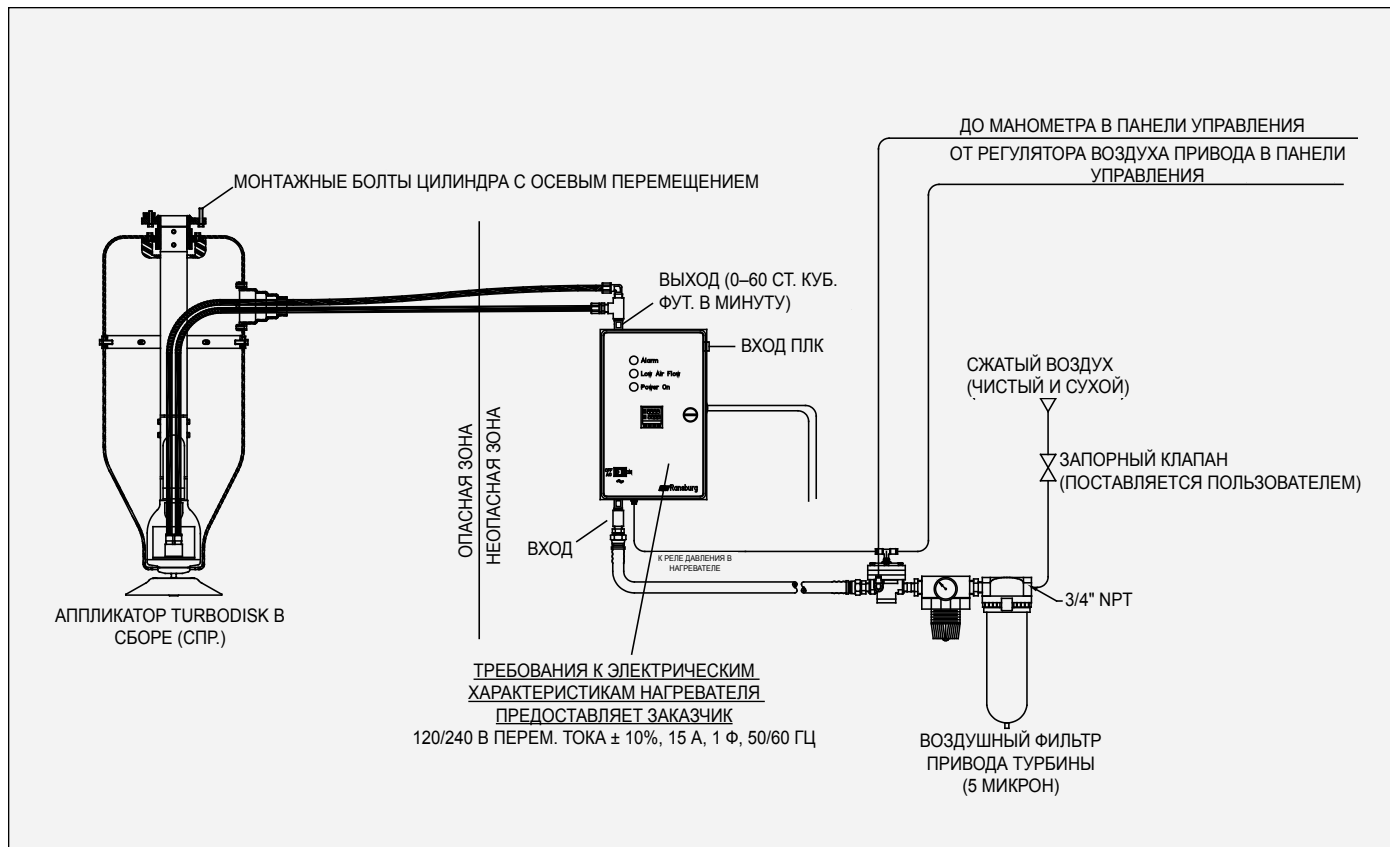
Воздухонагреватель и регулятор в сборе 78781-00
